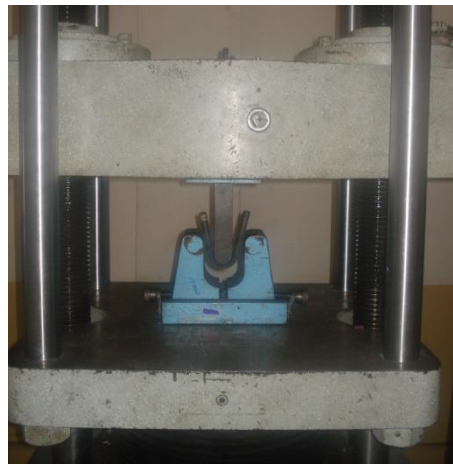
Máquina Universal-Tinius Olson – Ensayo de Doblado.
